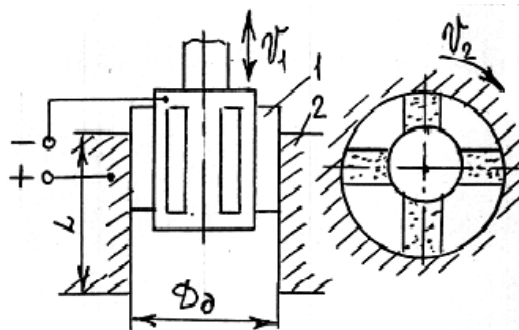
Схема хонінгування: 1 – інструмент; 2 – заготовка
